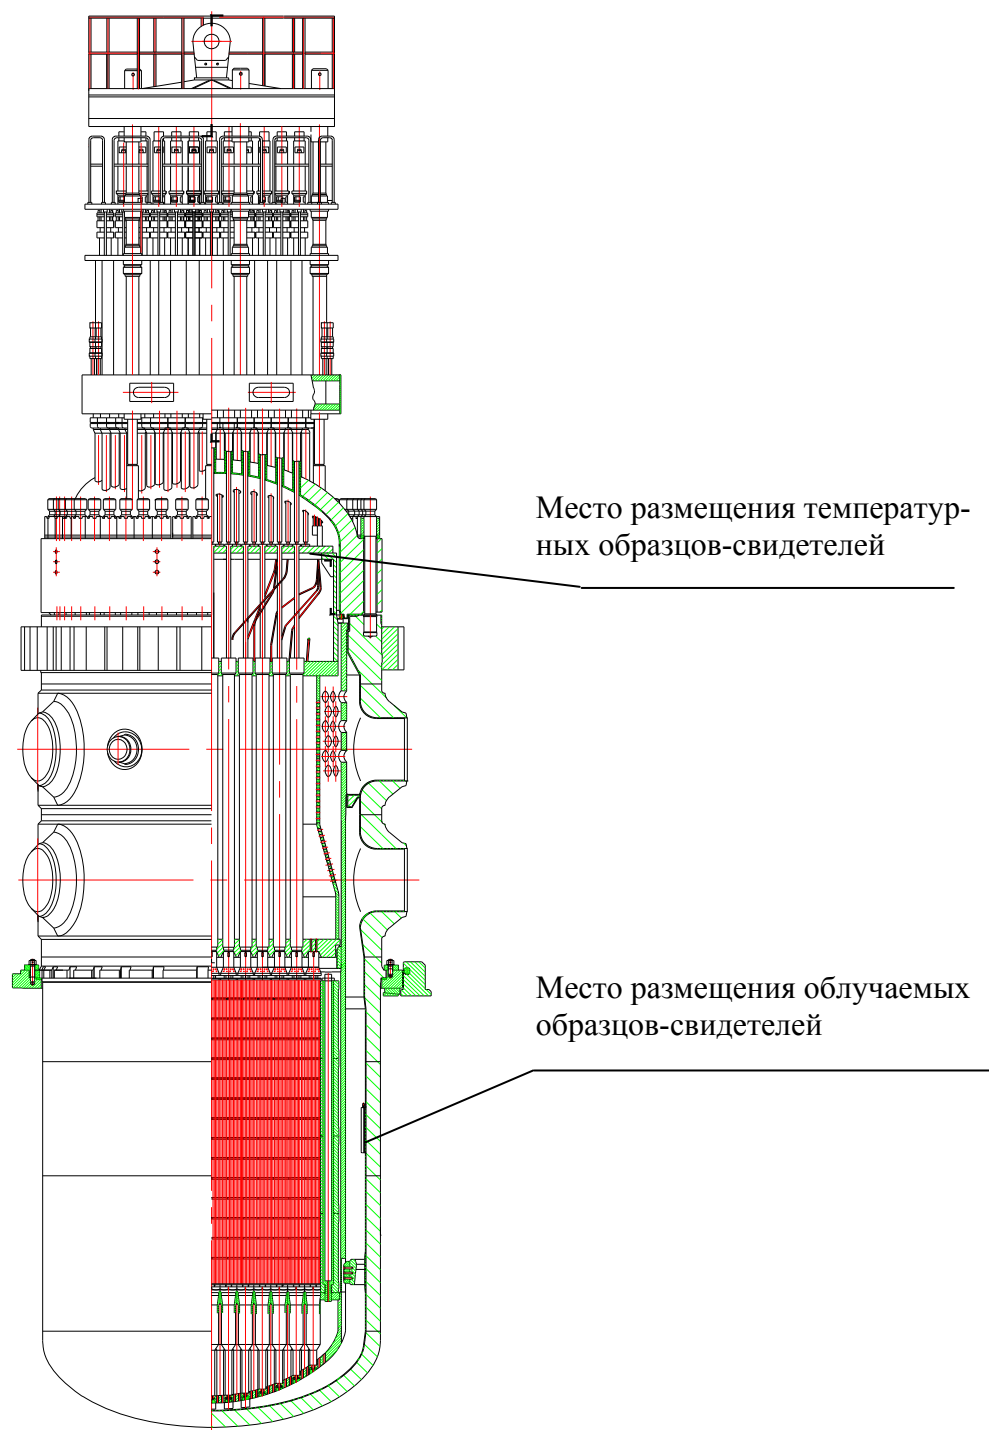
Расположение контейнерных сборок с образцами-свидетелями в корпусе реактора
